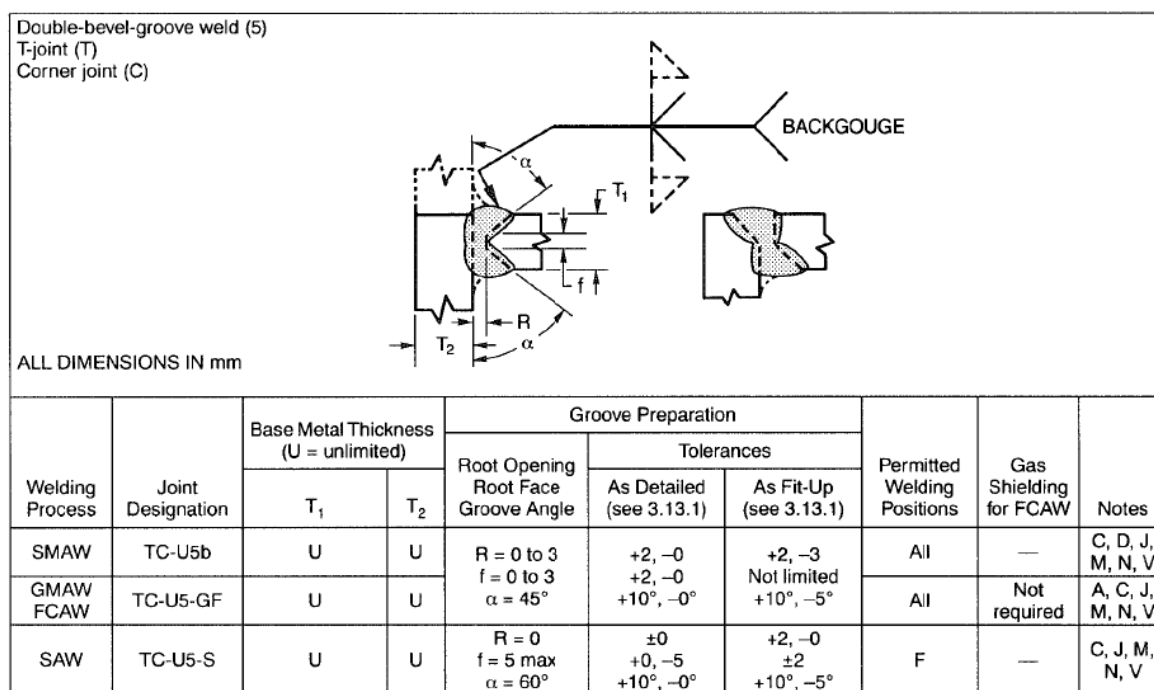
Soldadura a tope con doble bisel, unión T
